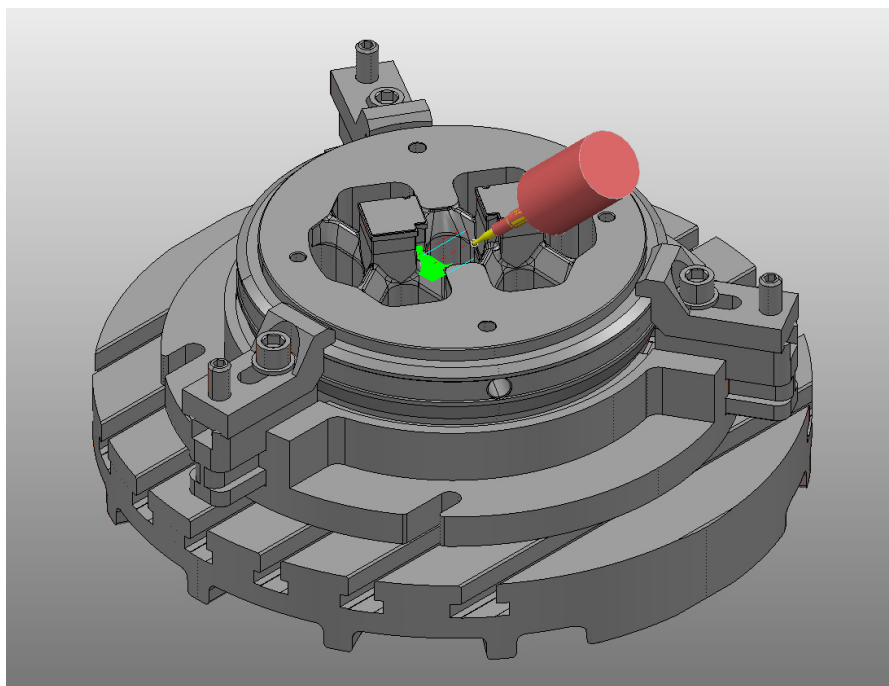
Участок фрезерной чистовой обработки рассекателя
